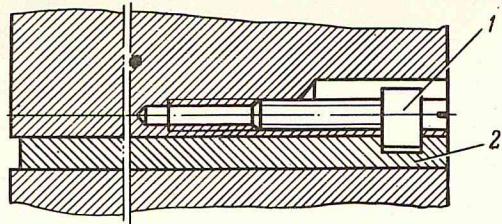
Регулировка зазора в направляющих верхнего суппорта
